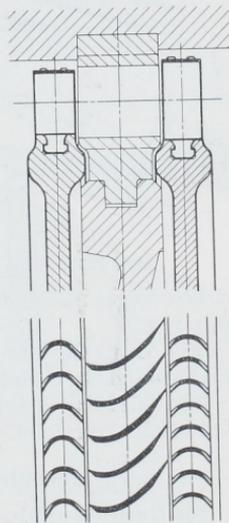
Turbine mit Blechschaufeln und Zwischenböden mit besonderen Kränzen.
